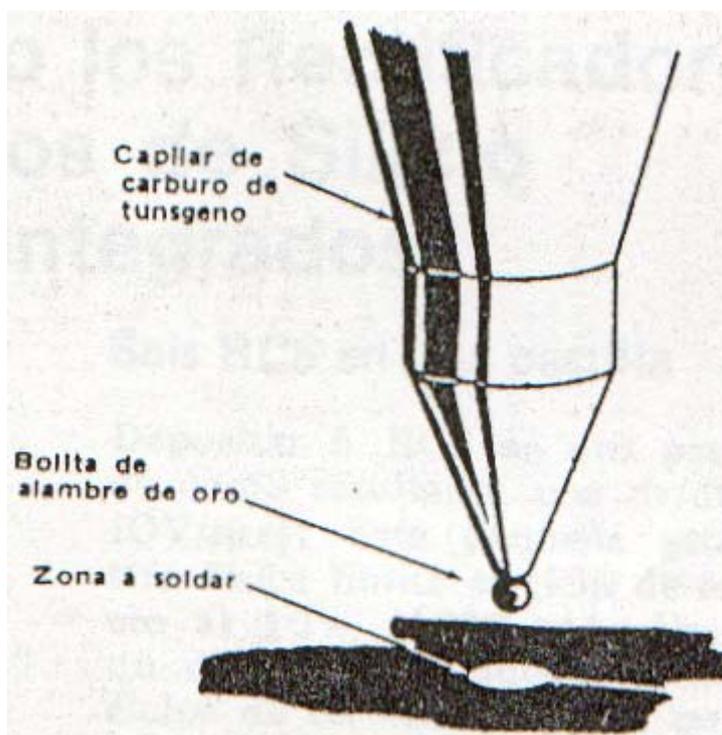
Soldadura por Termo compresión por Cabeza de Clavo usa una Bolita formada en el extremo de un alambre de Oro.
